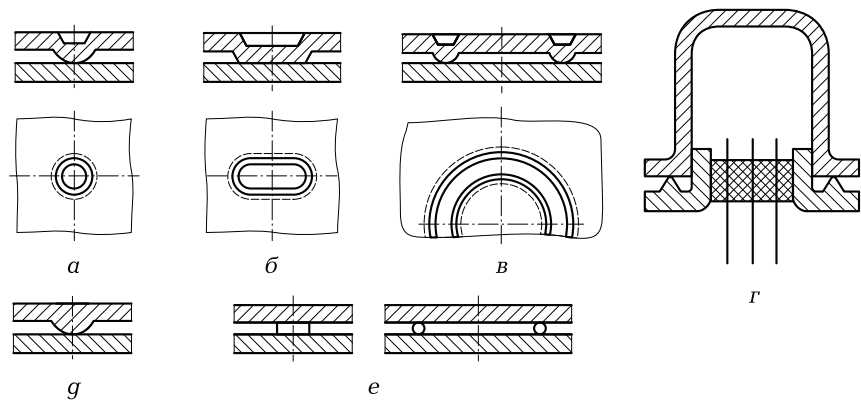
Типы рельефов при контактной рельефной сварке внахлестку:
